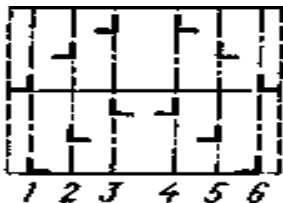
Размещение ножей на развёртке барабана фрезы
